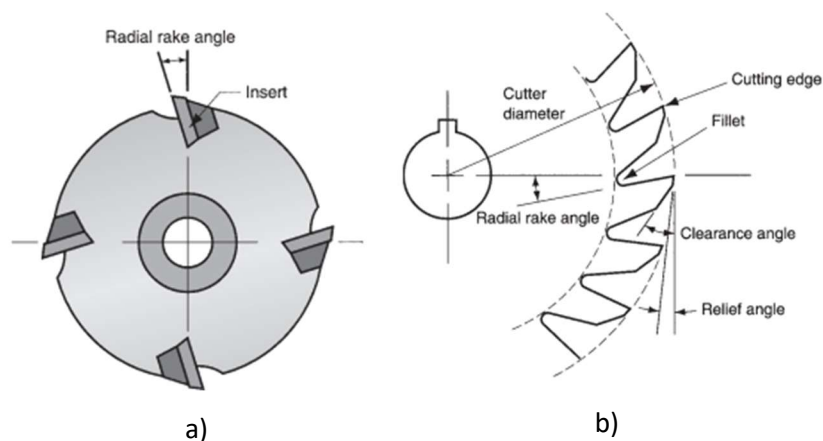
Geometria de ferramentas de corte: vista inferior de uma ferramenta de corte de topo a), Ferramenta de corte com 18 dentes b), adaptado de [8].
